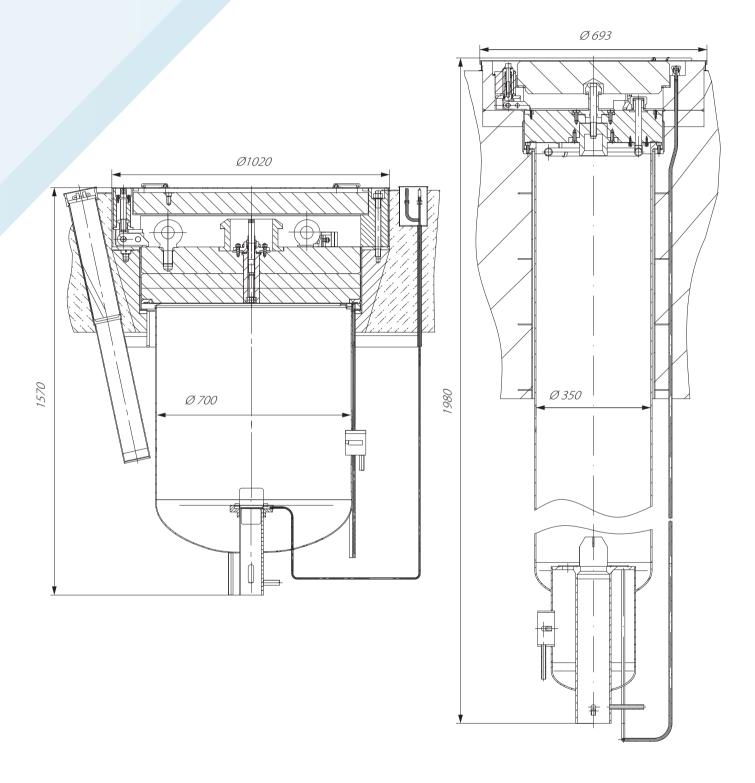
Общий вид камеры фильтра ФАРТОС-500, ФИБАН.
